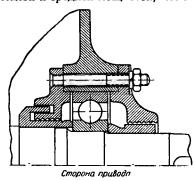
Подшипниковый узел с шарикоподшипником.
